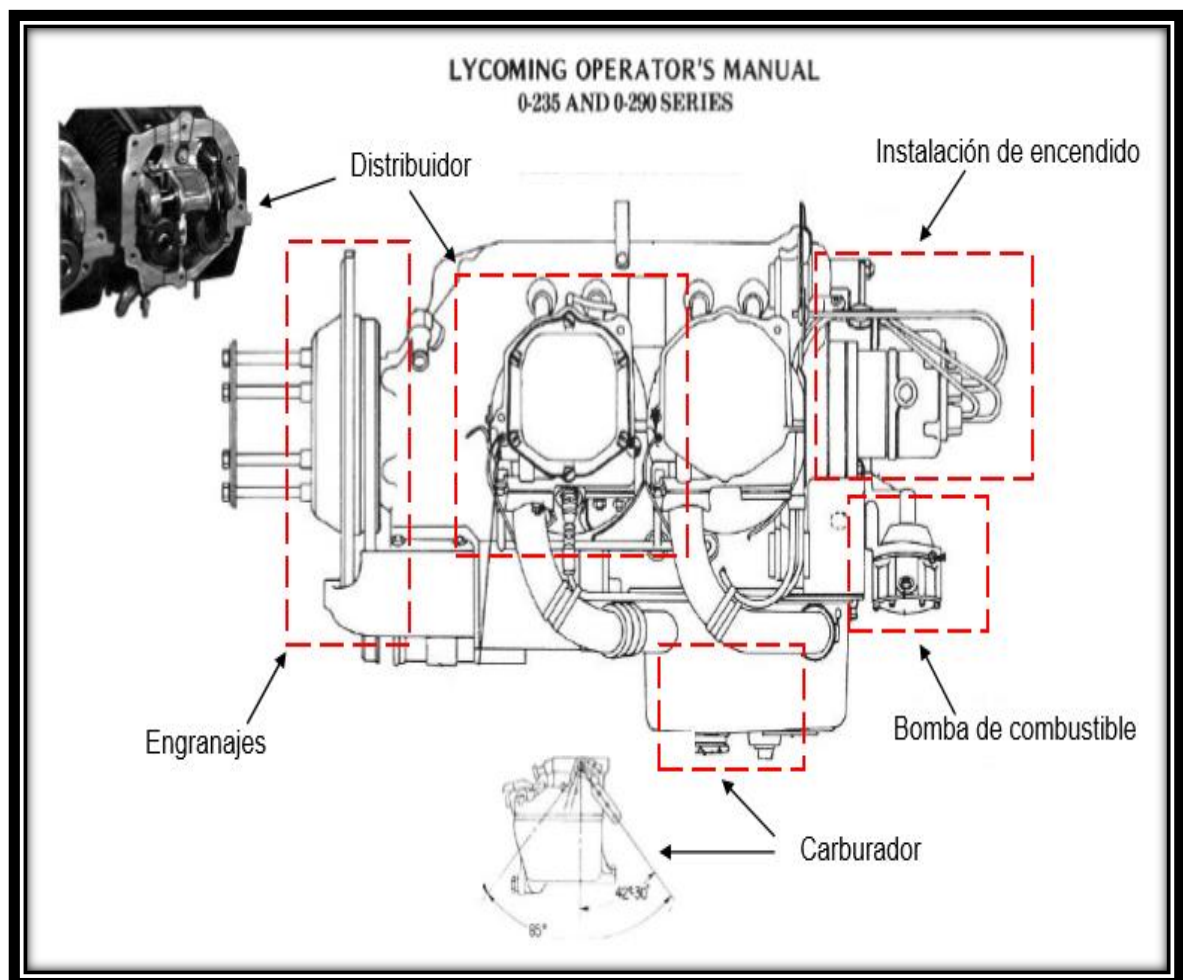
Motor reciproco Lycoming opuesto de 4 cilindros
